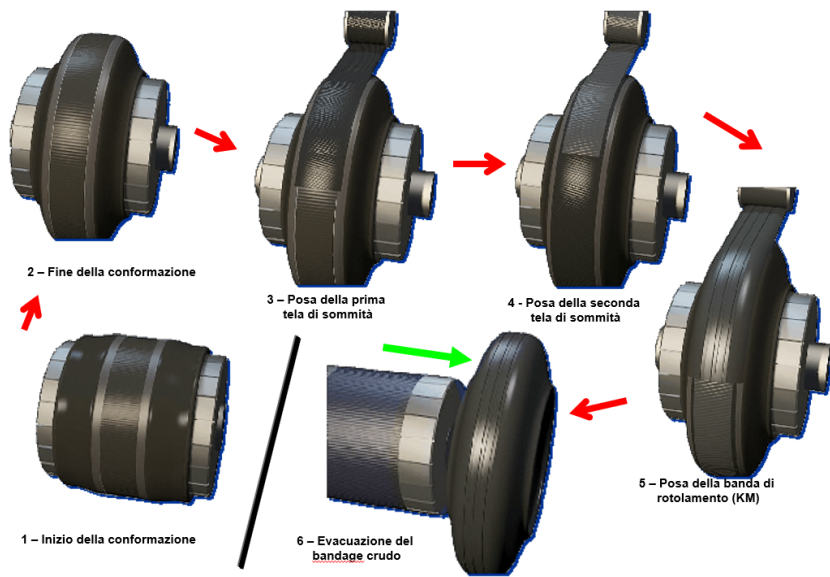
Seconda fase di assemblaggio di uno pneumatico
